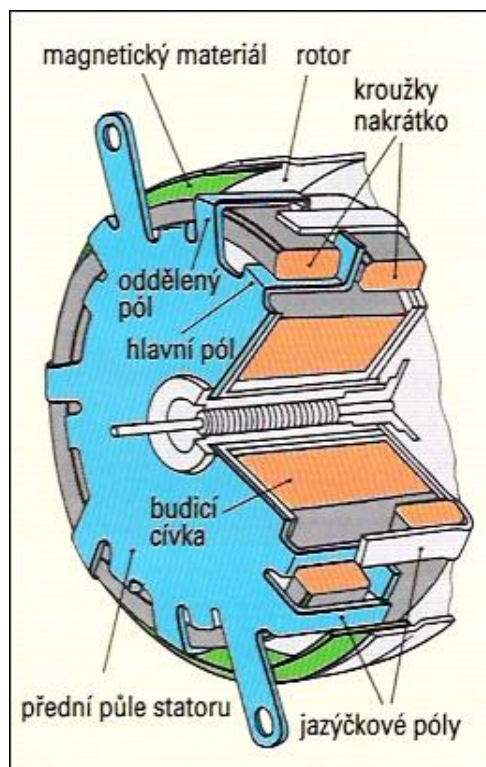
Motor se stíněnými póly v asymetrickém provedení (dvoupólovém)
